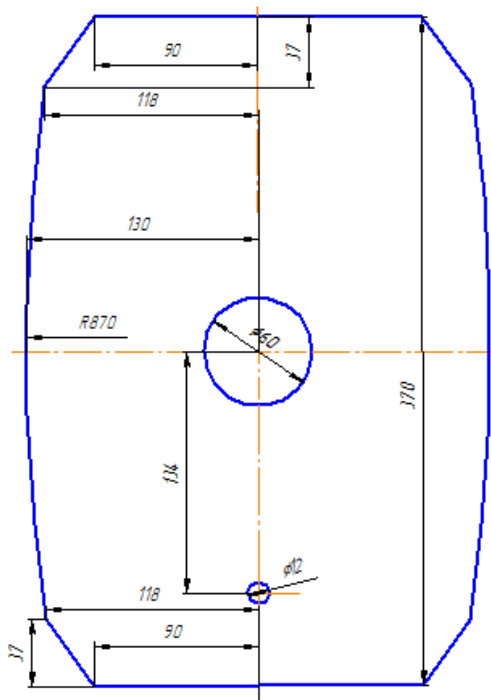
Шаблон вырубki плоской заготовки
